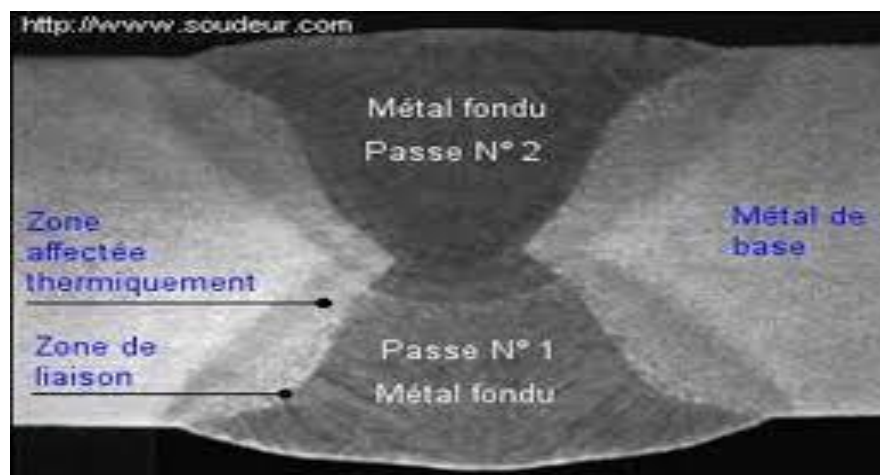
Présentation macrographique d'un joint soudé
